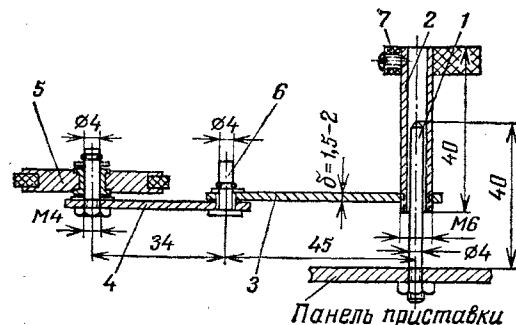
Размеры деталей привода обрезиненного ролика: 1 — ось привода; 2 — трубка; 3 — фиксирующий рычаг; 4 — рычаг; 5 — промежуточный ролик; 6 — ось соединения рычагов; 7 — ручка переключения скоростей.
